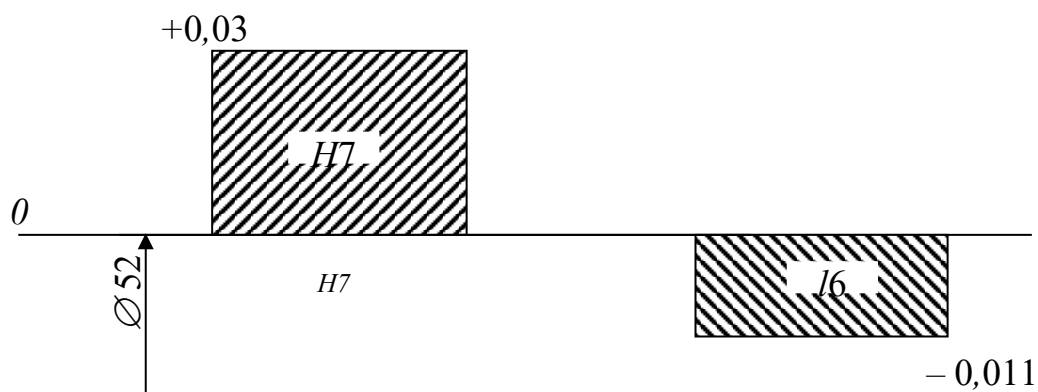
Посадка зовнішнього кільця підшипника підшипника
